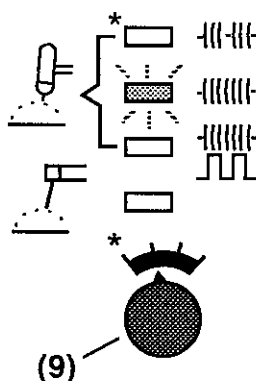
WIG-2-Takt-Schweißen - Heftschweißen
